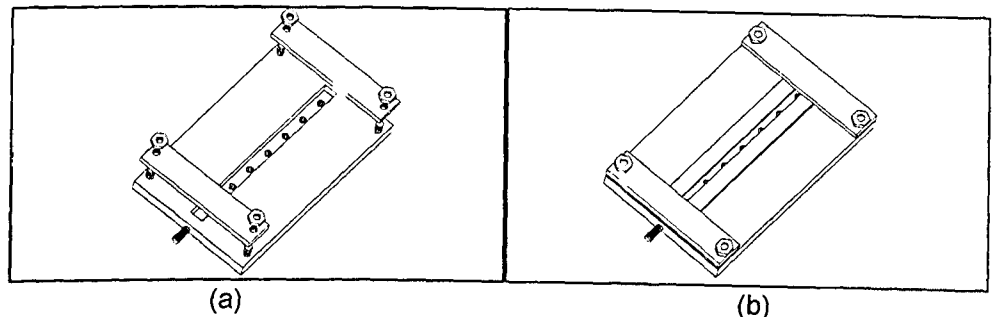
Esquemas do suporte de fixação para testes com gás de purga em perspectiva explodida (a) e montado (b), com dimensões de 295 x 190 x 25,4 mm
